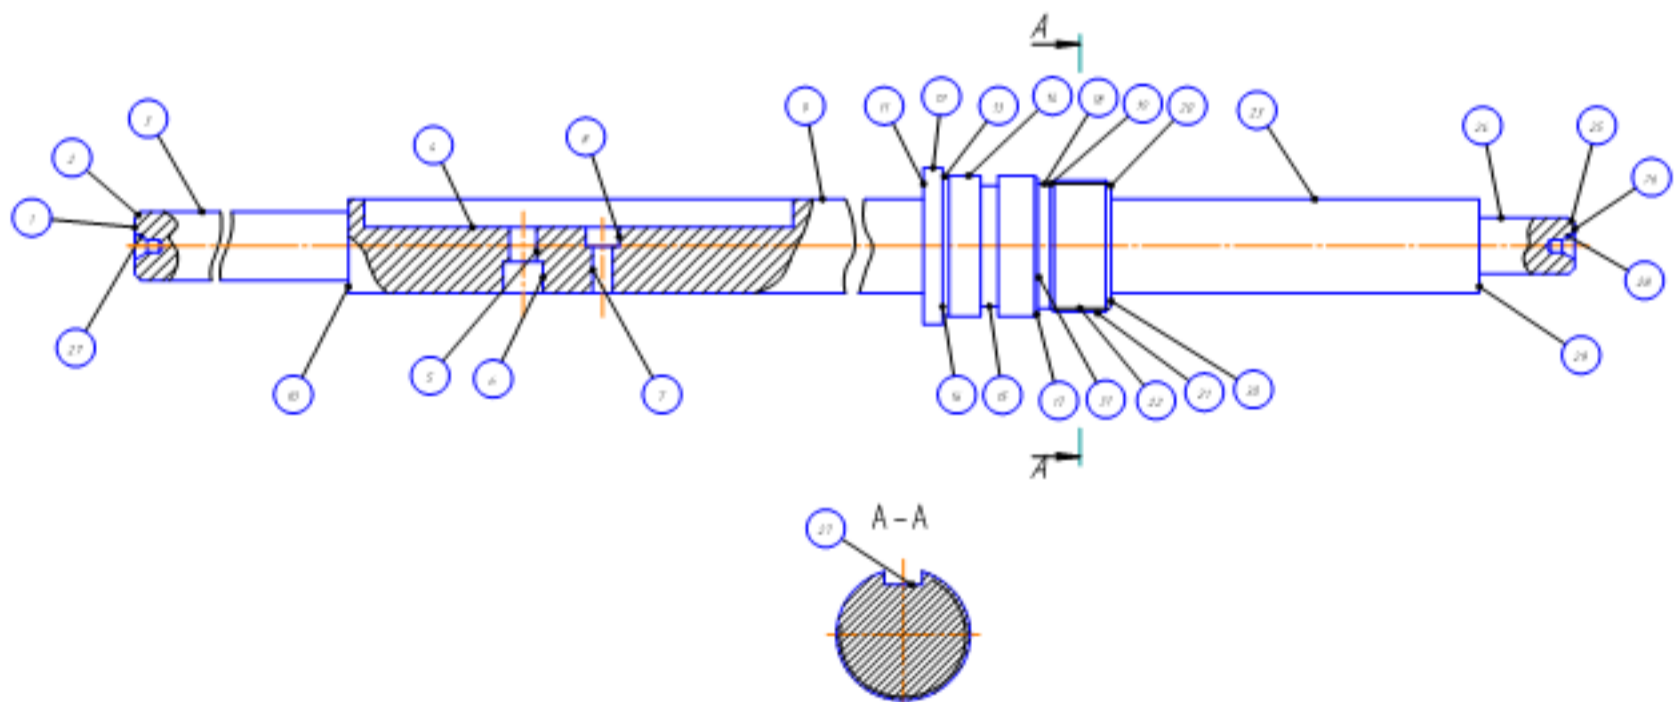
Креслення деталі з номерами поверхонь
